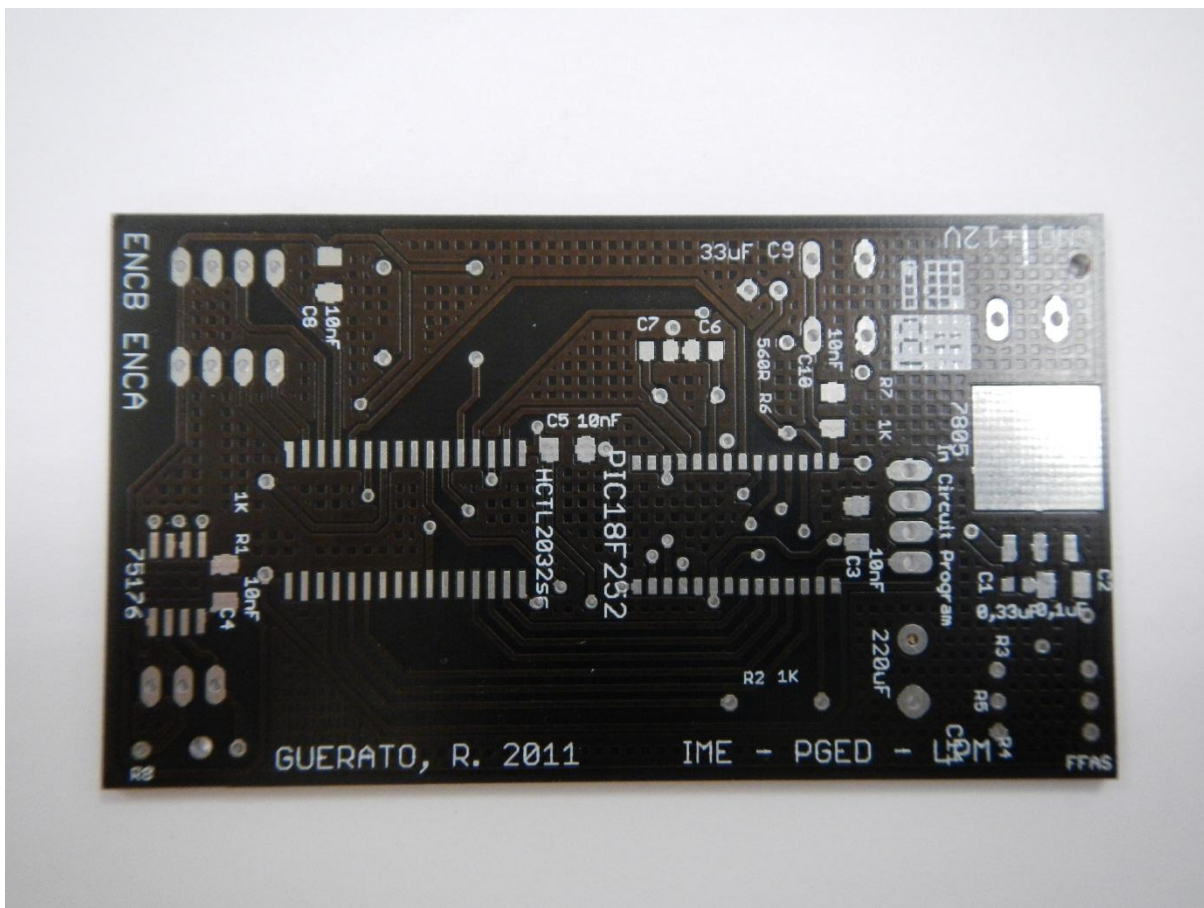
Placa de circuito Impresso pronta para a soldagem dos componentes.
